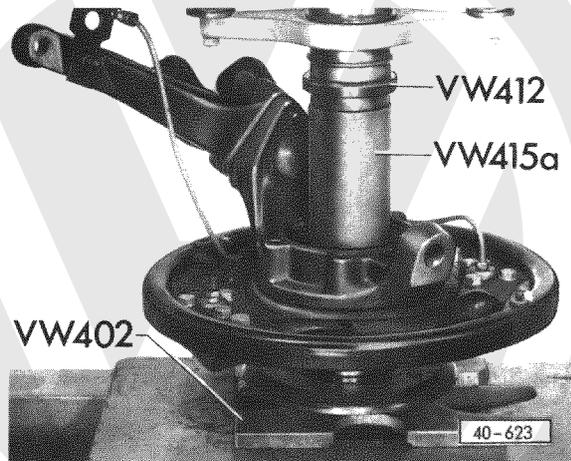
Äußeren Dichtring innen mit der Mutter für die Radnabe bis zum Anschlag nachpressen
